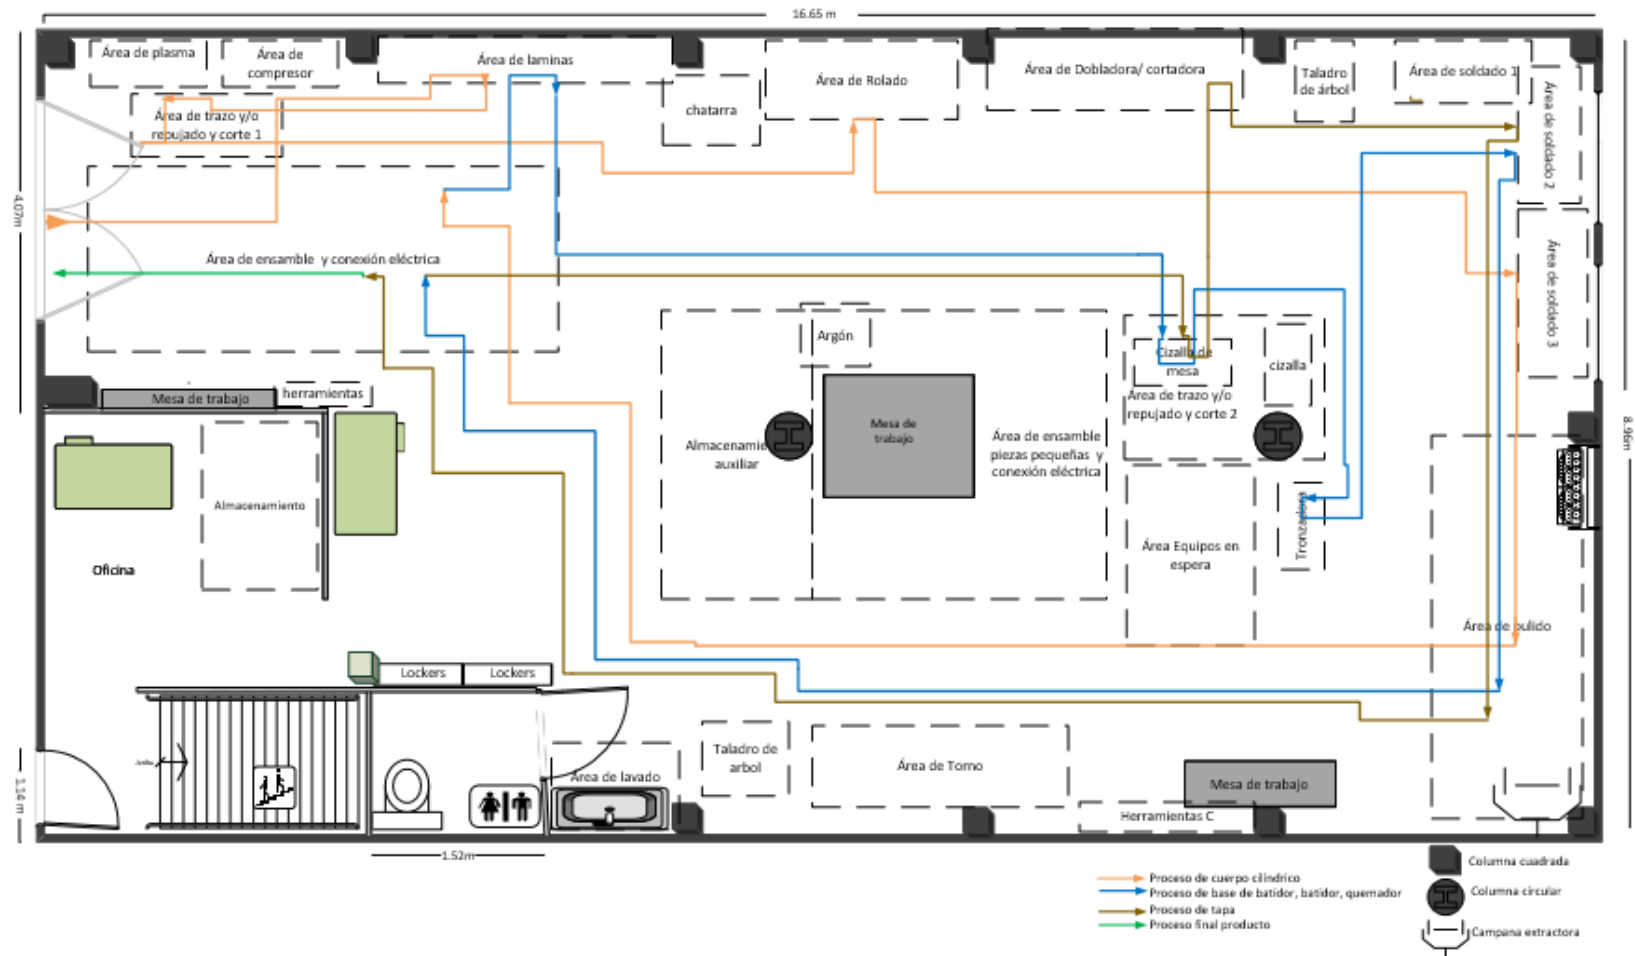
Propuesta de mejora de planta – plano reubicación de área
